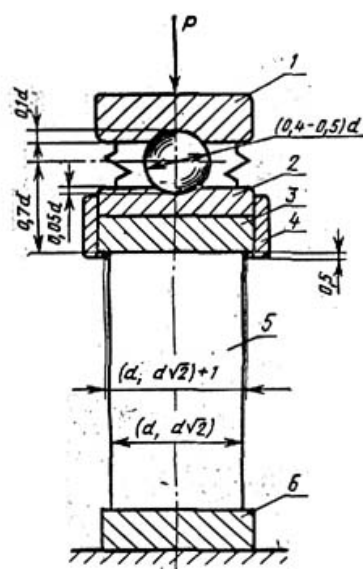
Схема приспособления для испытания на сжатие:
